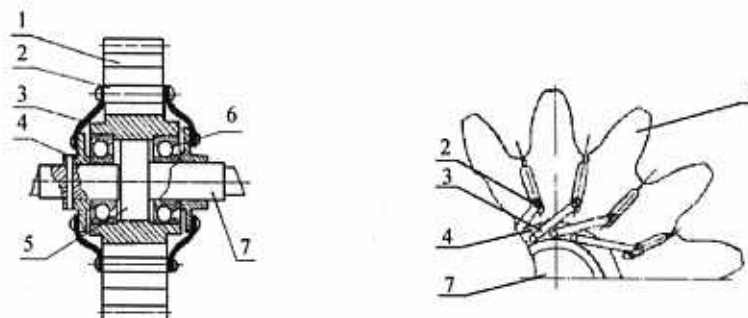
Общий вид зубчатого колеса: 1 – зубчатый венец с радиальными прорезями; 2 – ползун; 3 – гибкий шатун; 4 – ступица; 5 – упругий эластичный элемент; 6 – подшипник; 7 – вал [1]
